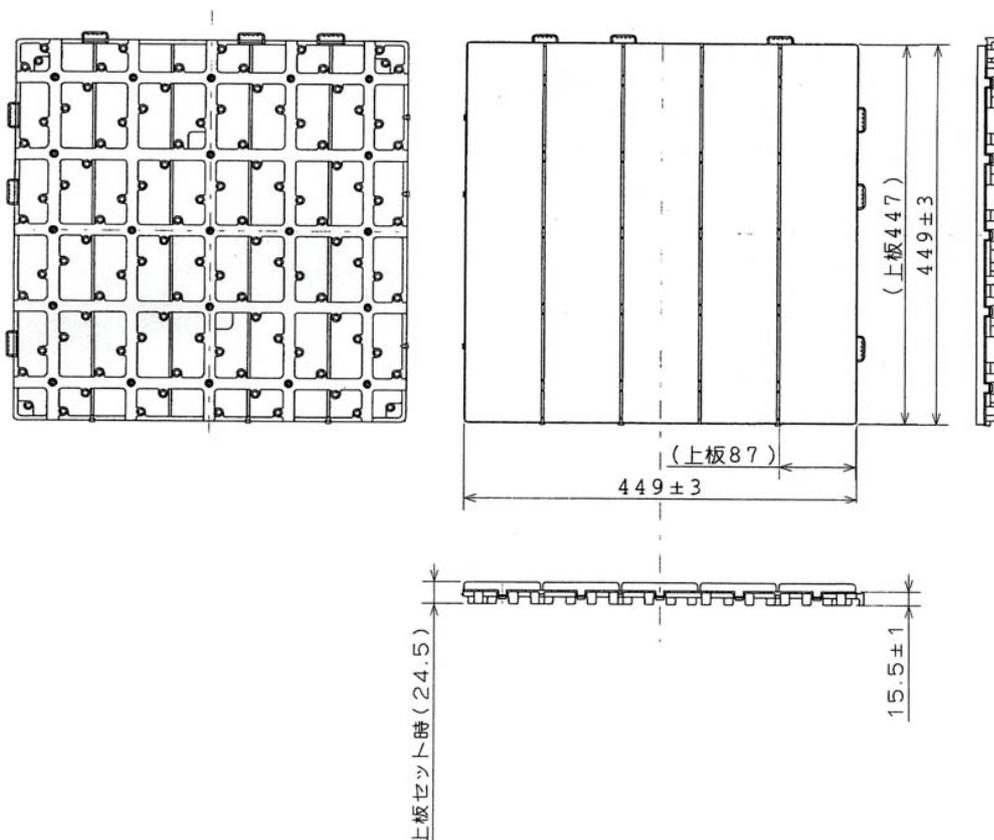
試験体図 (試験体 D : 直置き木粉入り樹脂タイプ)
